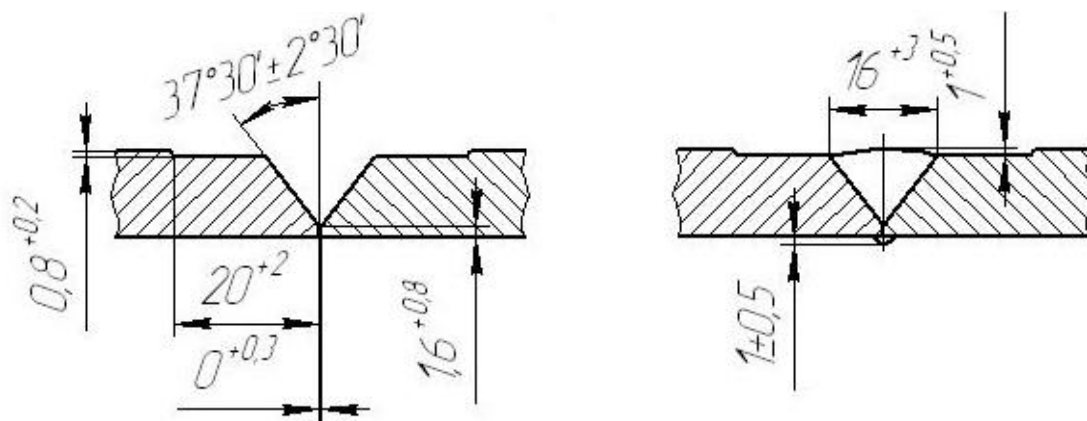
Подготовка кромок и форма сварного шва при выполнении стыкового кольцевого шва № 1
